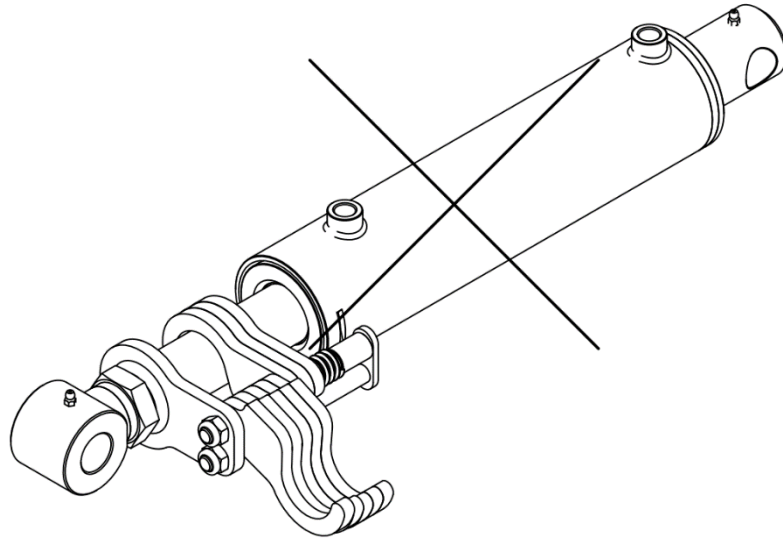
Installation incorrecte des cliquets sur la tige du piston du vérin. L'omission partielle de la fixation des cliquets à l'actionneur entraîne une répartition inégale des forces agissant sur la tige du piston et peut conduire à un flambage de la tige du piston et endommager l'ensemble du vérin. Une telle installation des cliquets est inadmissible !
